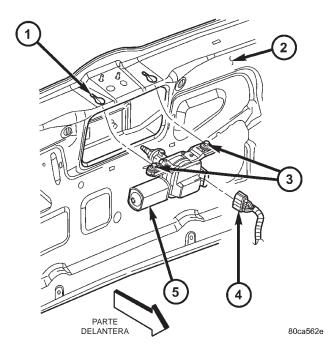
Desmontaje e instalación del motor del limpiador trasero
